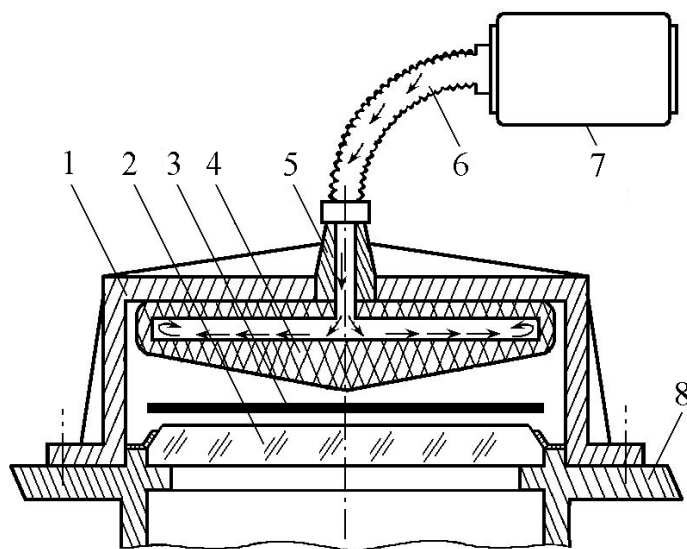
Пневмомеханічний пристрій вирівнювання аерофотоплівки з еластичною камерою
